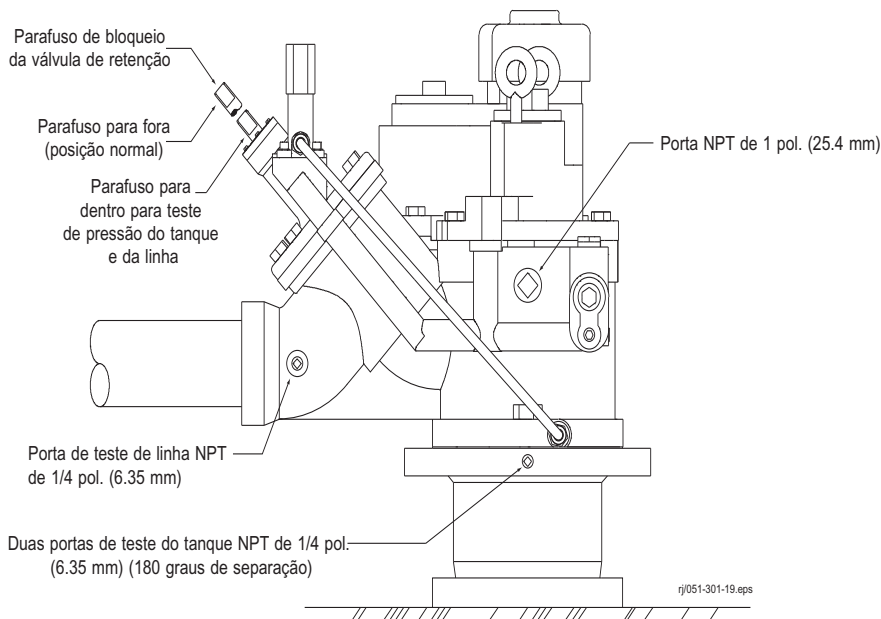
Montagem do manifold Maxxum®: Teste de linha e do tanque
